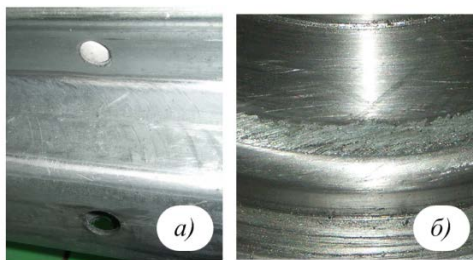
Повреждение покрытия заготовки (а) и налипание цинка на формирующие валки
